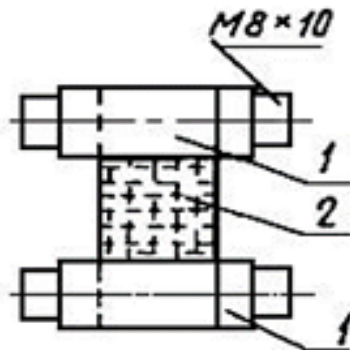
Схема испытания на сжатие по ГОСТ 4651-2014.1 – приспособление для крепления образца; 2 – образец.
